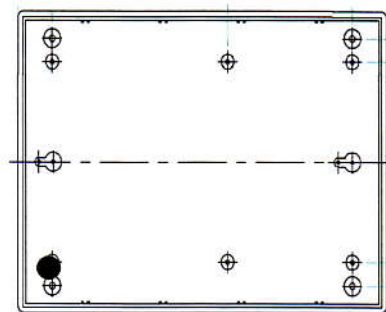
Корпус отсчетного устройства, вид снизу
